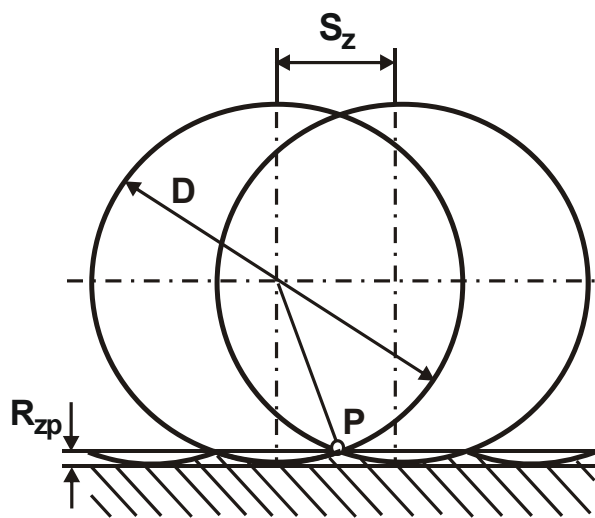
Расчетный микропрофиль обработанной поверхности при фрезеровании цилиндрической фрезой
